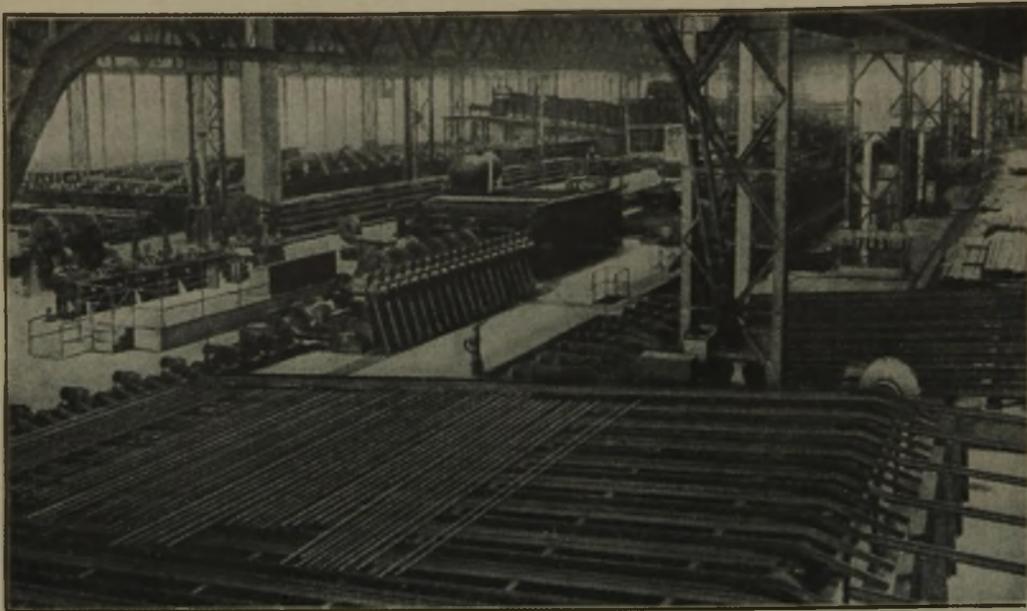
Reduzierwalzwerk mit Rohrkühlbett.
